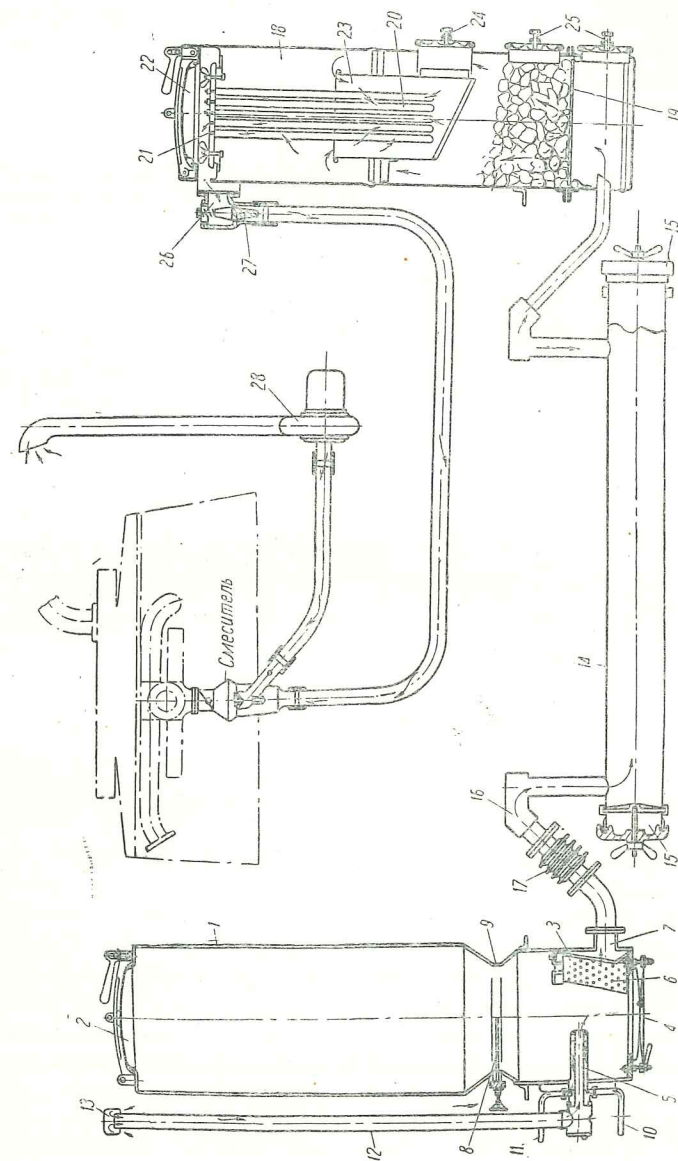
Схема газогенераторной установки НАТИ Г-23 для автомобиля ЗИС
